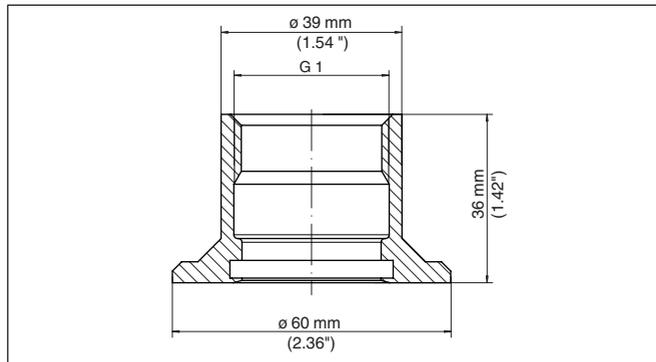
Dimensions raccord à souder G1 (DIN 3852-A)
